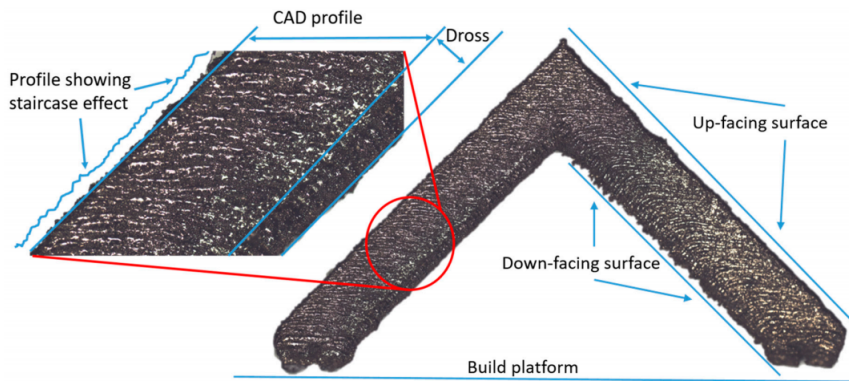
Etat de surfaces issues du procédé SLM [5].
